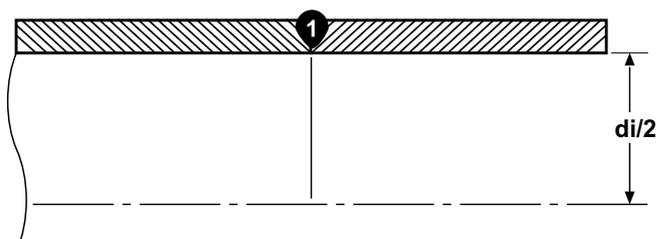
Soldadura a tope tipo "V" (Para diámetros mayores, se usará soldadura a tope tipo "X")
